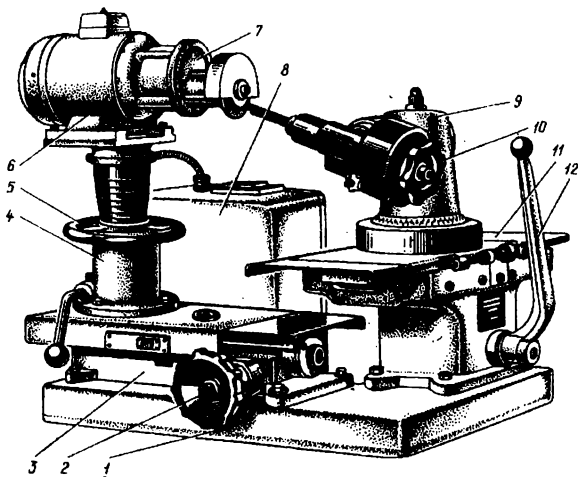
Станок ТчФК для заточки концевых фрез
